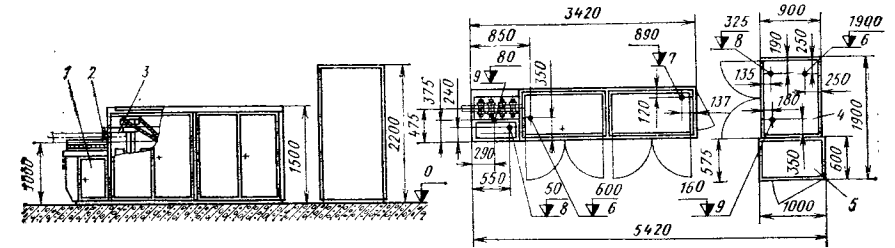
Рекомендуемая планировка размещения кузнечного нагревателя:
